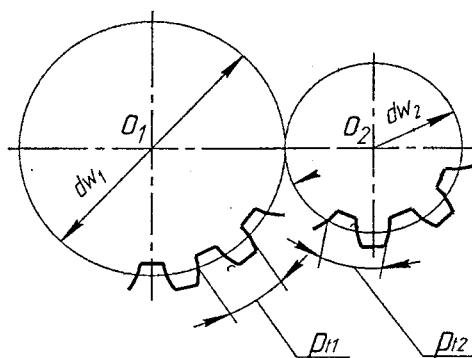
Початкові циліндри (*pitch cylinder*) зачеплення (*gearing*)
